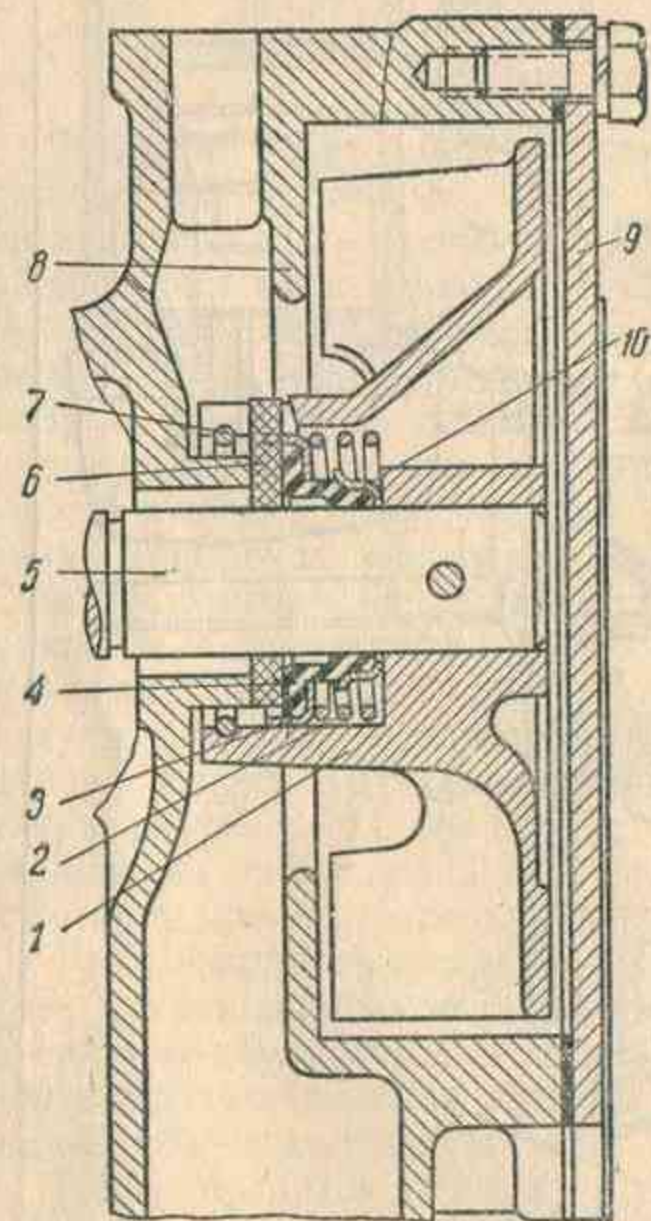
Сальник водяного насоса: 1 — крыльчатка насоса; 2 — пружина; 3 — обойма манжеты; 4 — резиновая манжета; 5 — валик насоса; 6 — текстолитовая шайба; 7 — пружинное кольцо; 8 — корпус насоса; 9 — крышка корпуса; 10 — обойма манжеты
